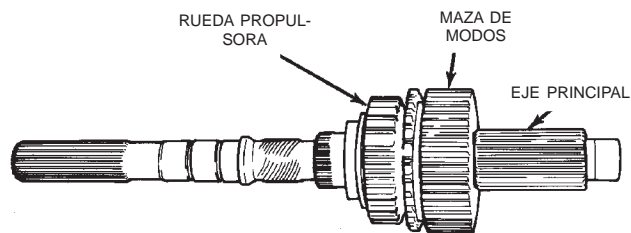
Instalación de conjunto de horquilla y maza de posiciones
